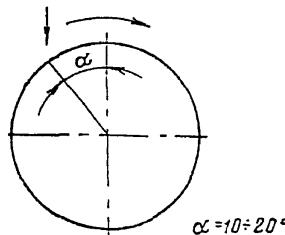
Смещение горелки при сварке кольцевых швов
